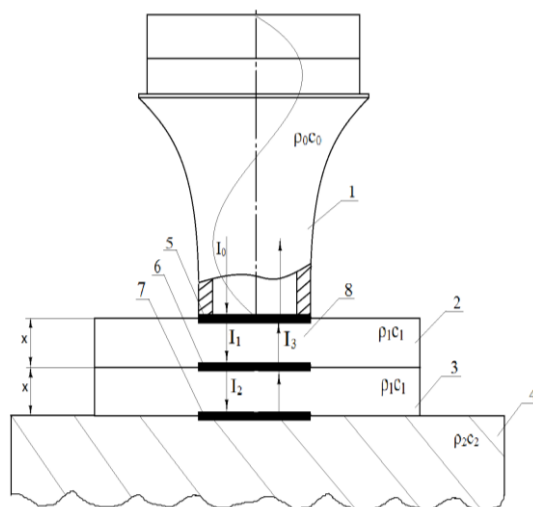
Схема процесса УЗ кольцевой сварки.
